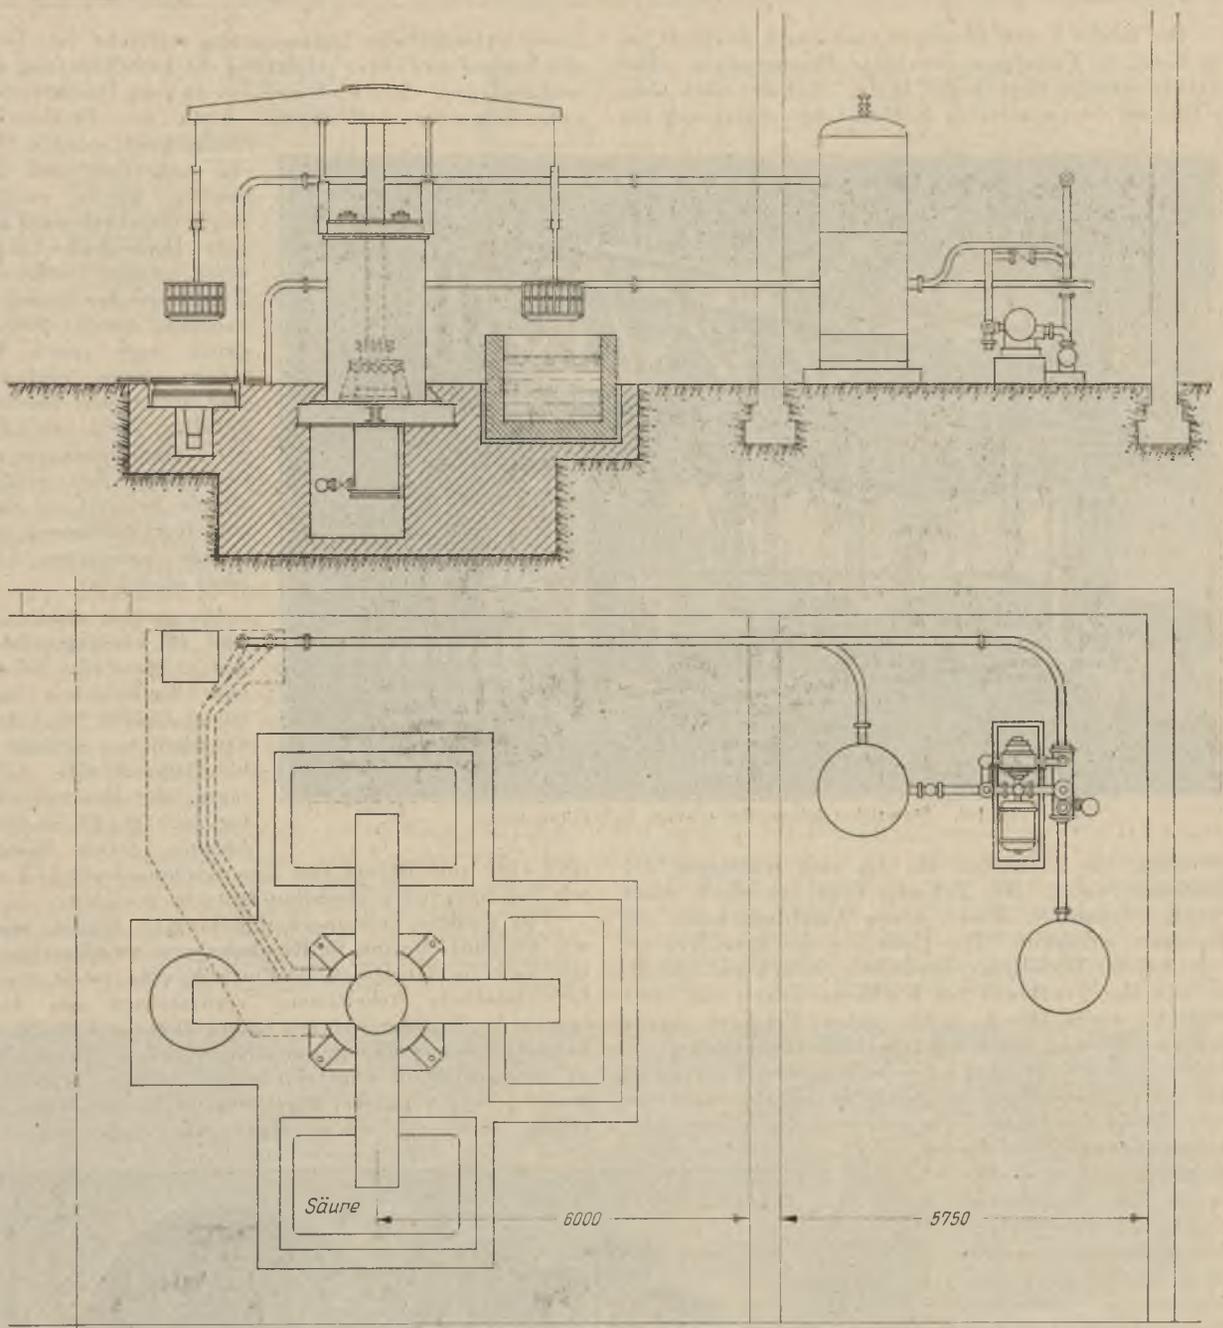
Plan einer Turmbeizanlage nach Bild 9.
